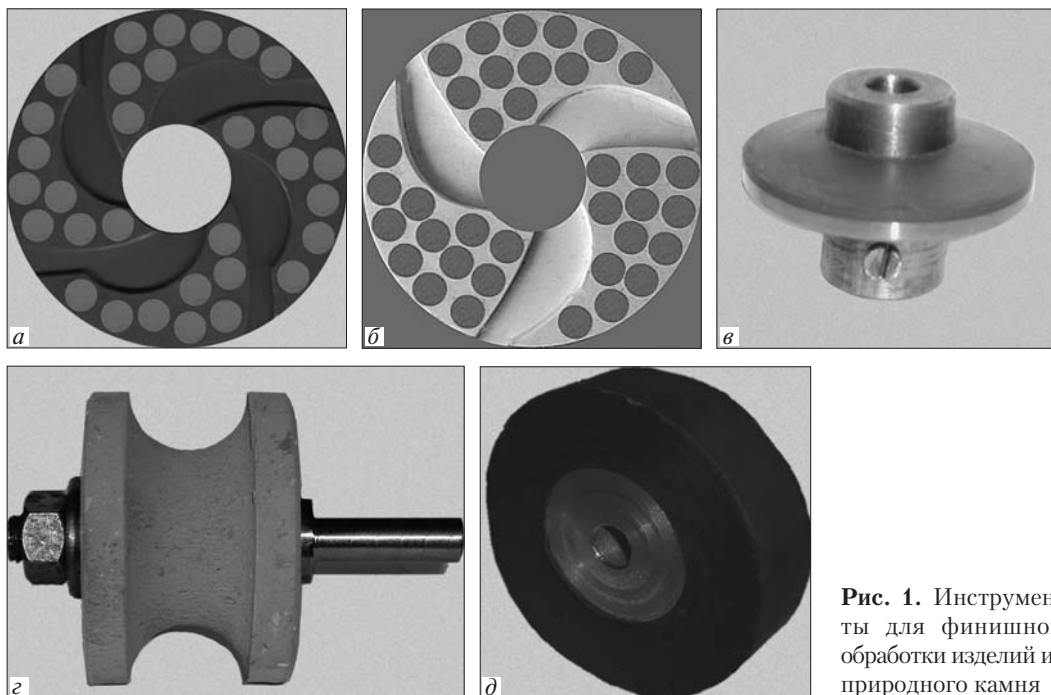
Інструменти для фінішної обробки изделий из природного камня
